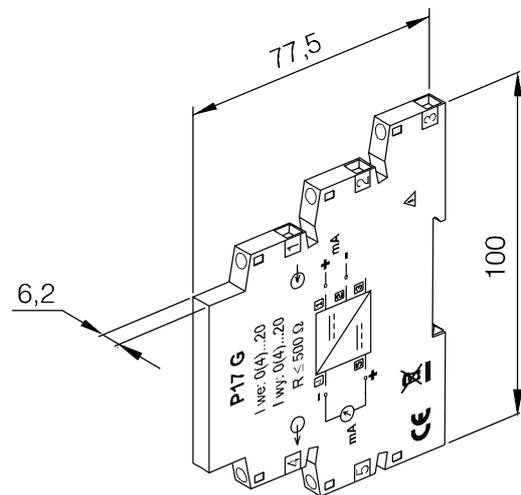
Vue et dimensions de l'isolateur de boucle HCG17
